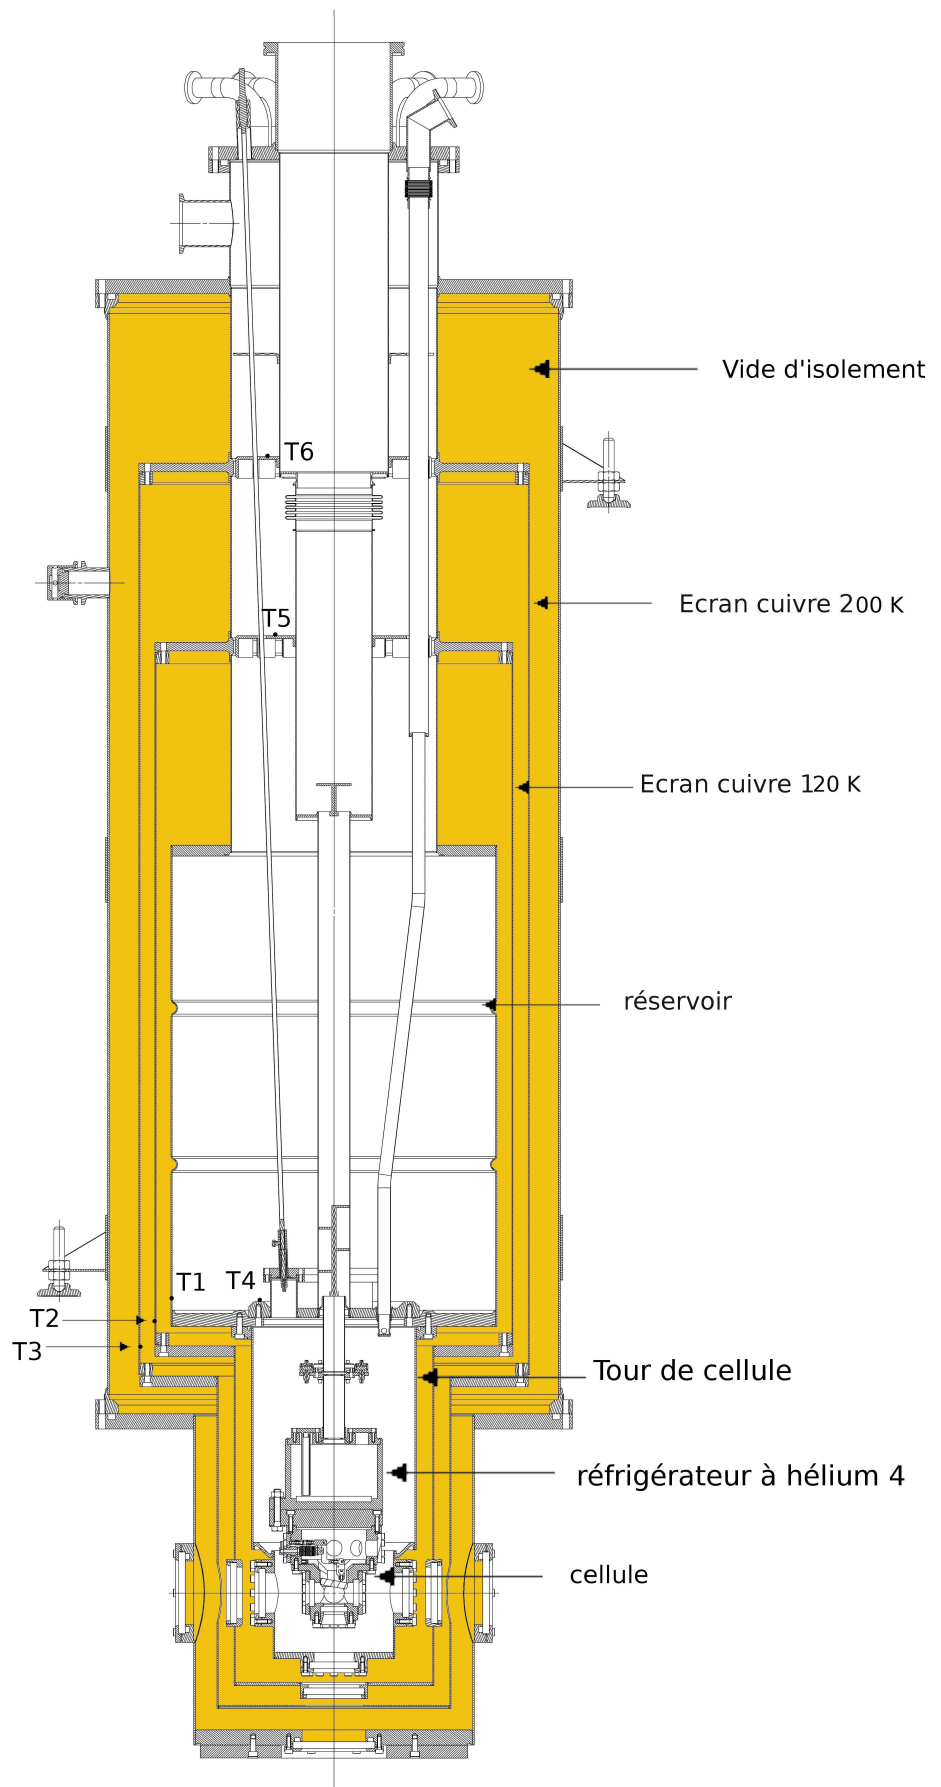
Vue en coupe du cryostat (Echelle : 1/7).
